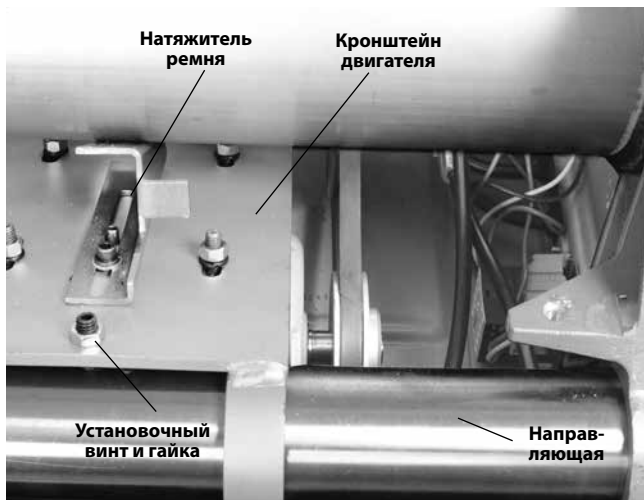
Кронштейн двигателя и натяжитель ремня
